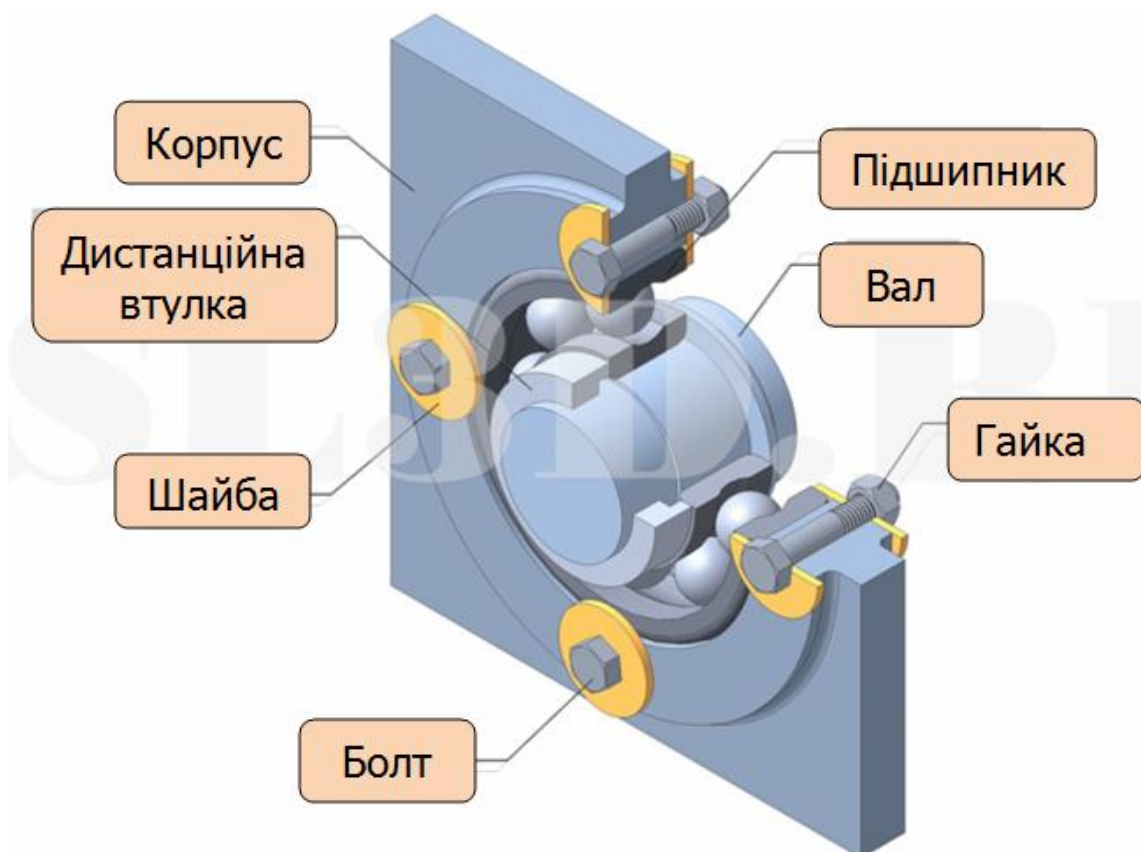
Установка підшипника з допомогою окремих шайб
